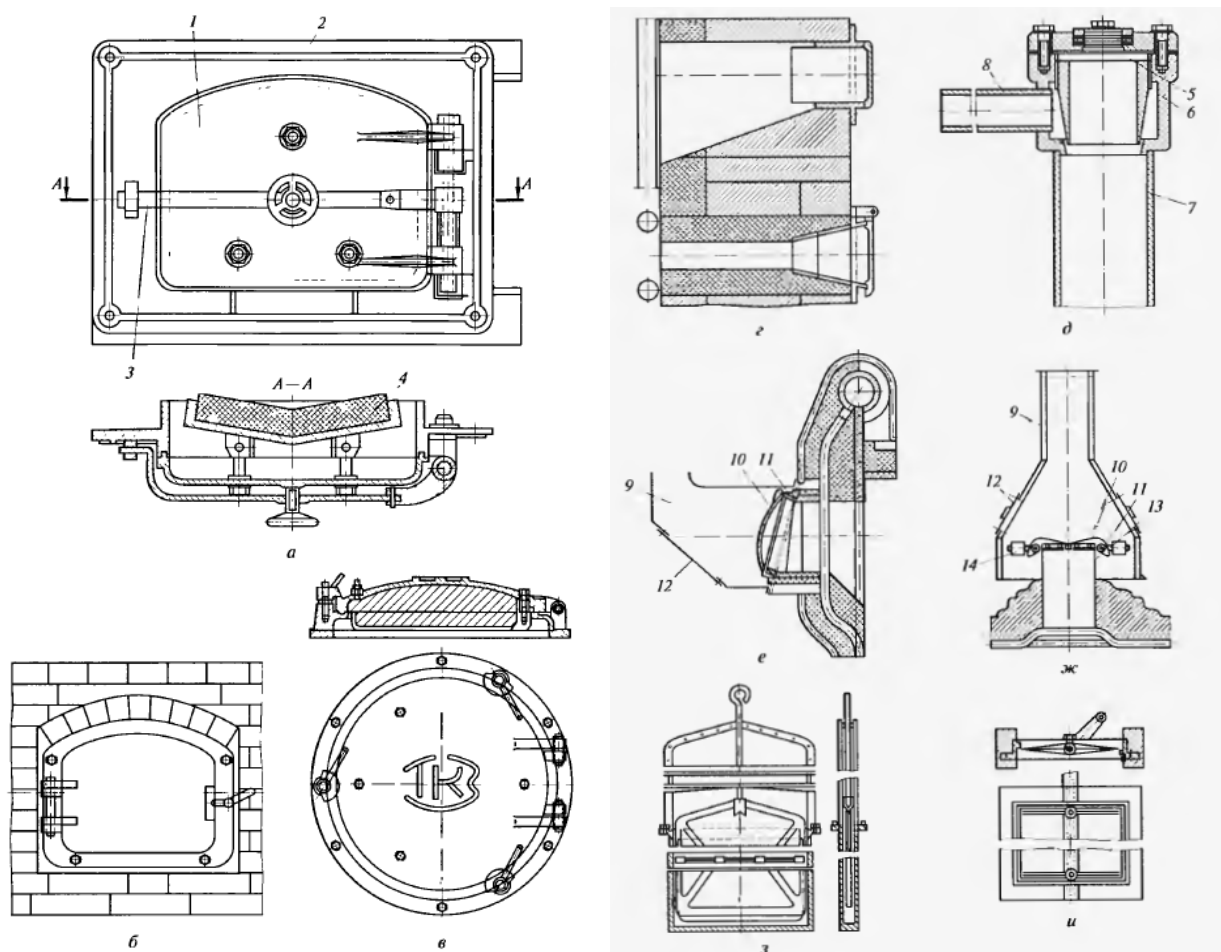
Гарнитура котла: а – дверца с уплотнением и обмурованным металлическим экраном к топочной камере; б,в – лазы прямоугольной и круглой формы в обмуровке; г,д – гляделки для топочных камер и газоходов (г – под разряжением; д – под наддувом); е,ж – взрывные клапаны для установки в боковых стенах и потолке котельного агрегата; з – шибер; и – поворотная заслонка; 1 – дверца; 2 – рама; 3 – щеколда; 4 – экран; 5 – стекло; 6,11 – корпус; 7 – патрубок; 8 – труба для подвода воздуха; 9 – отводящий короб; 10 – створка клапана; 12 – люк; 13 – рычаг; 14 – груз.
